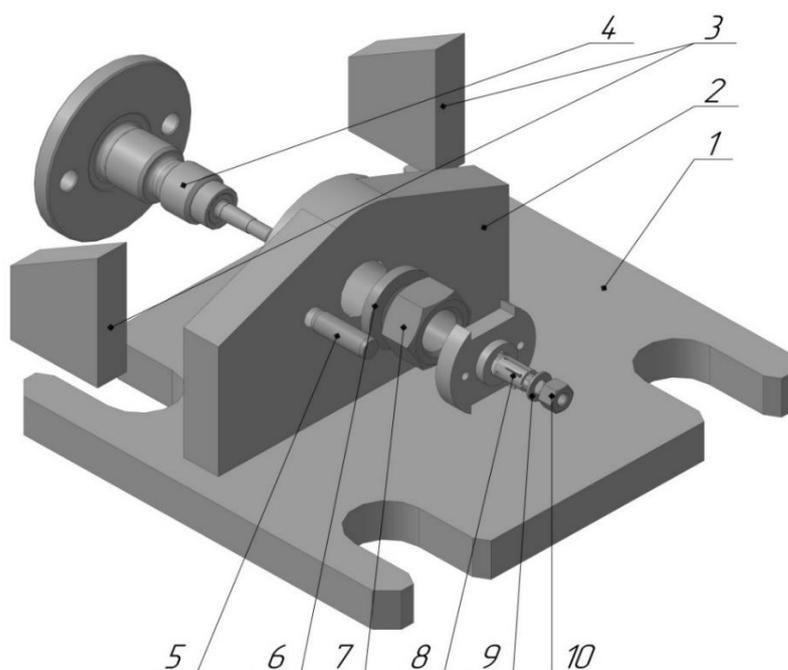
специальное станочное приспособление для фрезерной операции в разборе.
